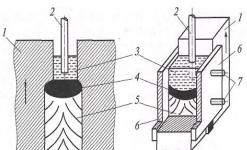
Схема процесса электрошлаковой сварки: 1 — свариваемая деталь; 2 — электрод; 3 — расплавленный металл; 4 — сварочная ванна; 5 — сварной шов; 6 — подвижные ползуны-кристаллизаторы; 7 — подвод охлаждающей воды; стрелками показано направление сварки
